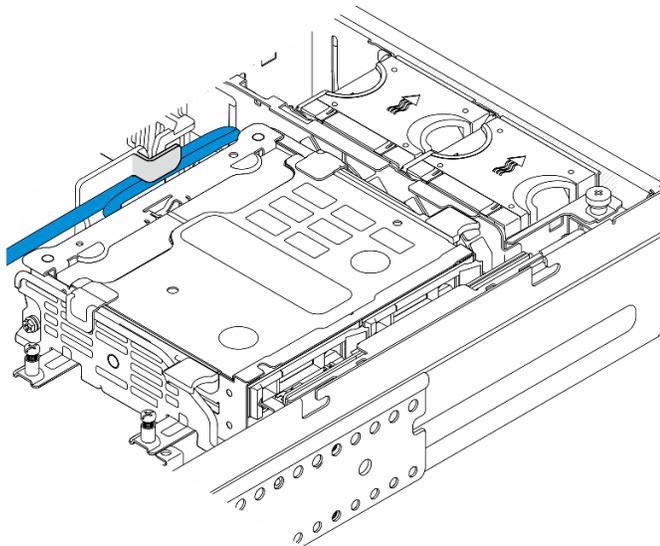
Cables asegurados por el clip para cables del deflector de aire del procesador
